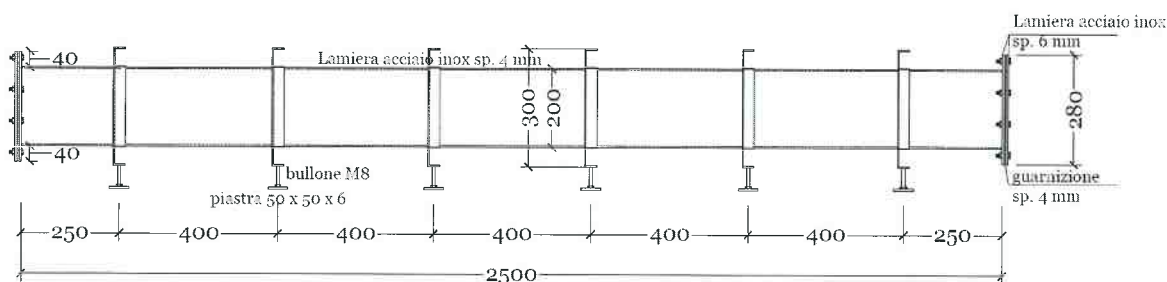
Prospetto laterale di uno "spezzone" di tubazione
